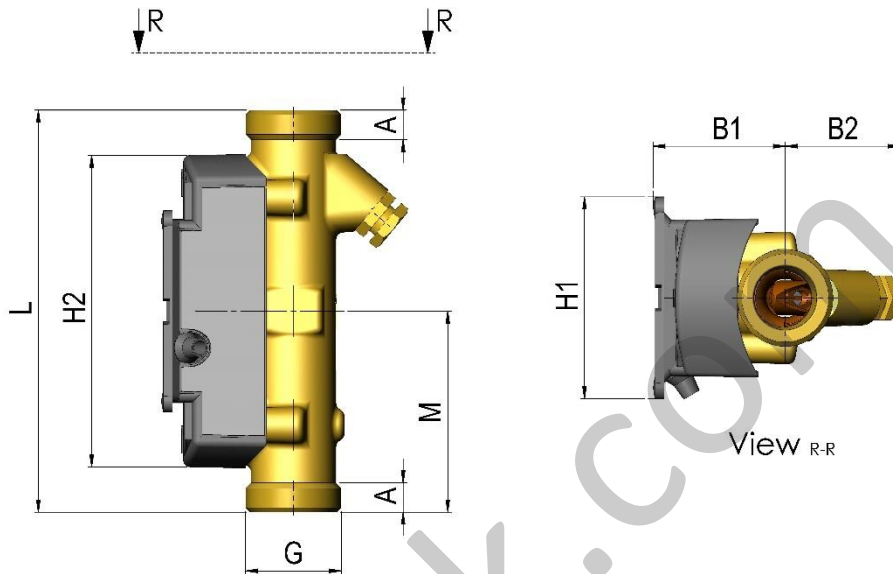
Размерные чертежи ULTRAFLOW® 54 с резьбовым соединением типа 65-5-XXHX-XXX.
